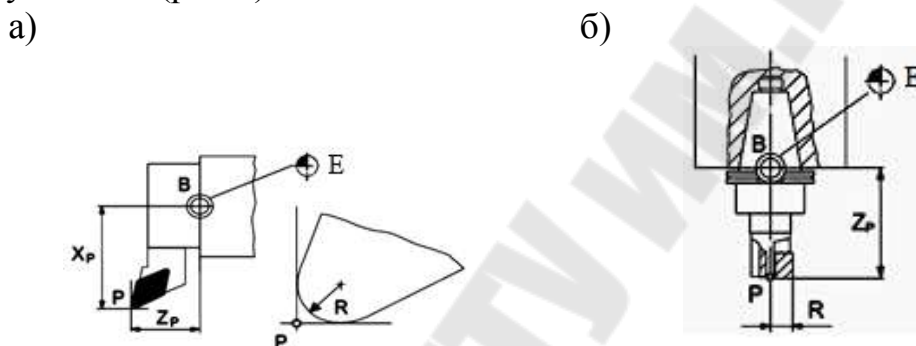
Расположение точки установки (B) и нулевой точки (N) на токарном (а) и фрезерном (б) станках с ЧПУ
